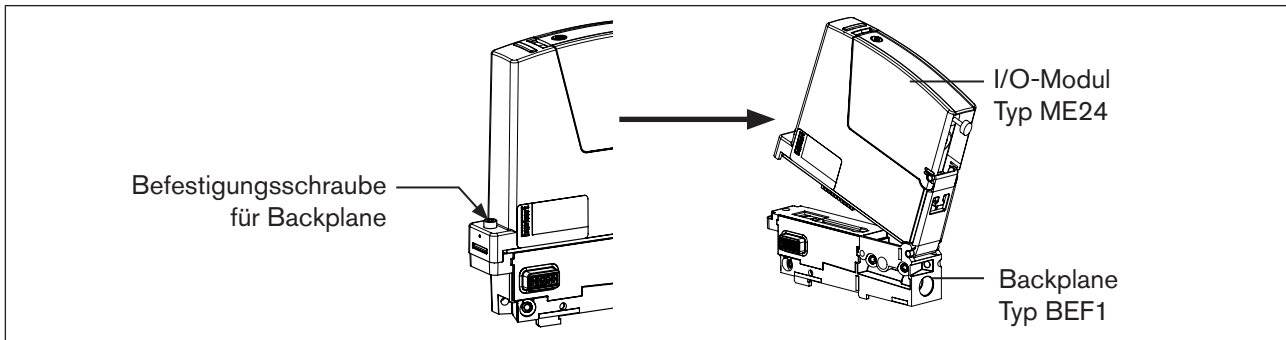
Gerätetausch, I/O-Modul Typ ME24
